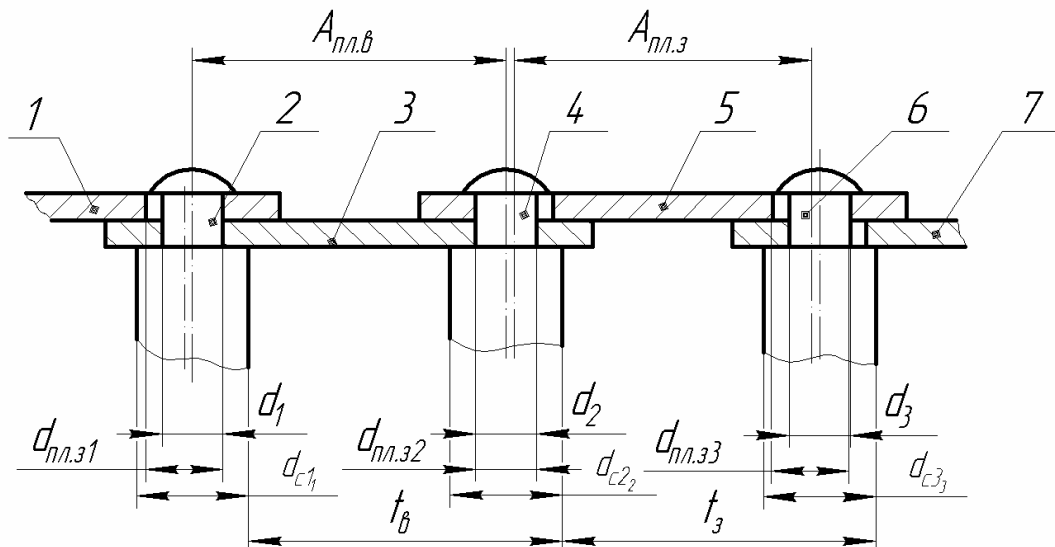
Розрахункова схема для визначення полів допусків на контактні кроки при з'єднанні співвісних валиків ПТБЛ з отворами внутрішніх пластин з натягом, а з отворами зовнішніх пластин із зазором: 1,5 – зовнішні пластини; 2,4,6 – валики; 3,7 – внутрішні пластини
